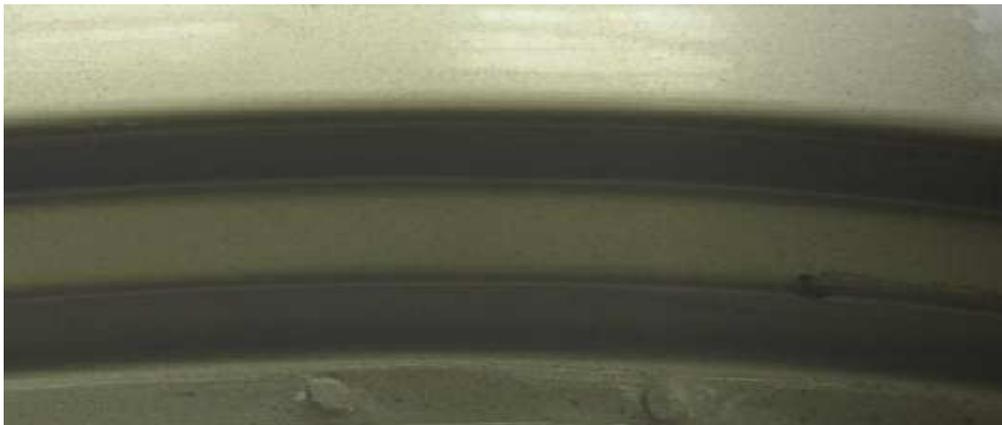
Soldadura por puntos de resistencia
